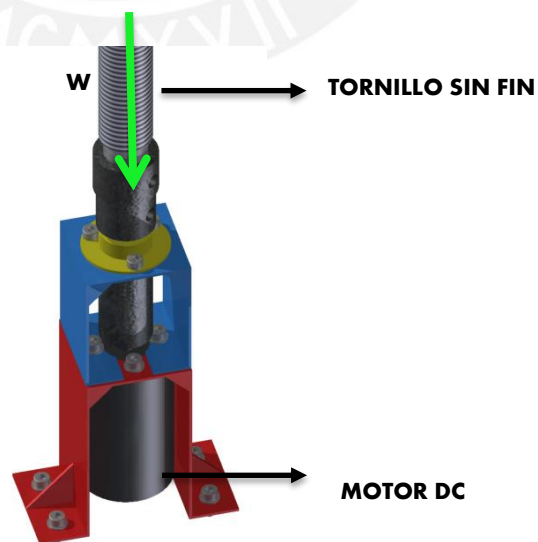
Ensamble de motor DC con tornillo sin fin. Fuente: Propia
